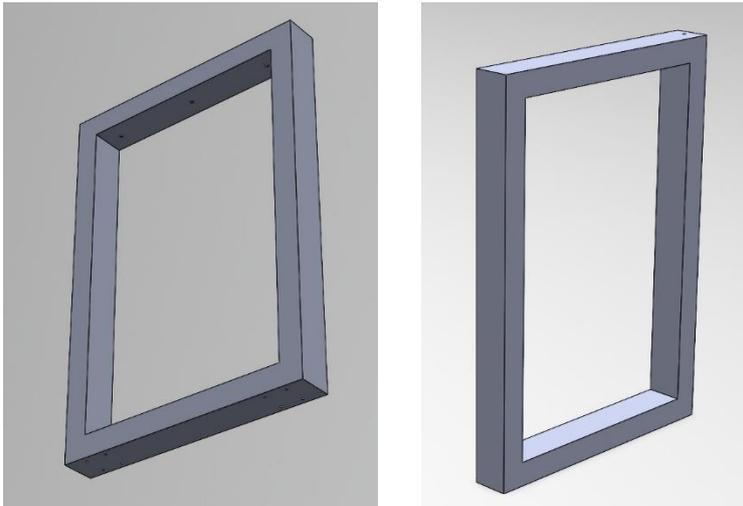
Modelado piezas 2.1-2.2. Elaboración propia (2023).
